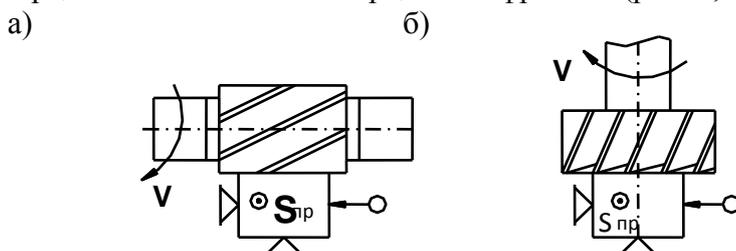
Схемы фрезерования горизонтальных поверхностей.
